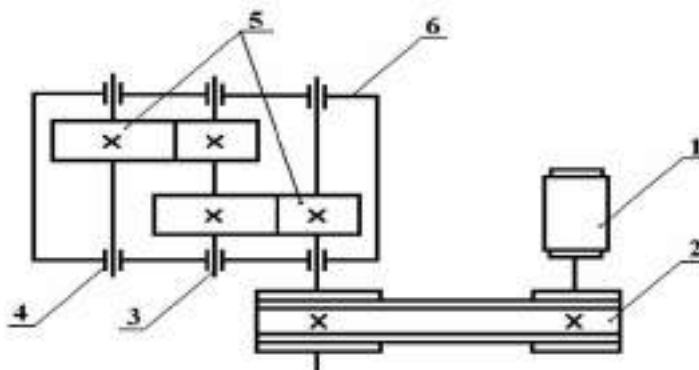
Кинематическая схема привода с цилиндрическим зубчатым редуктором:
